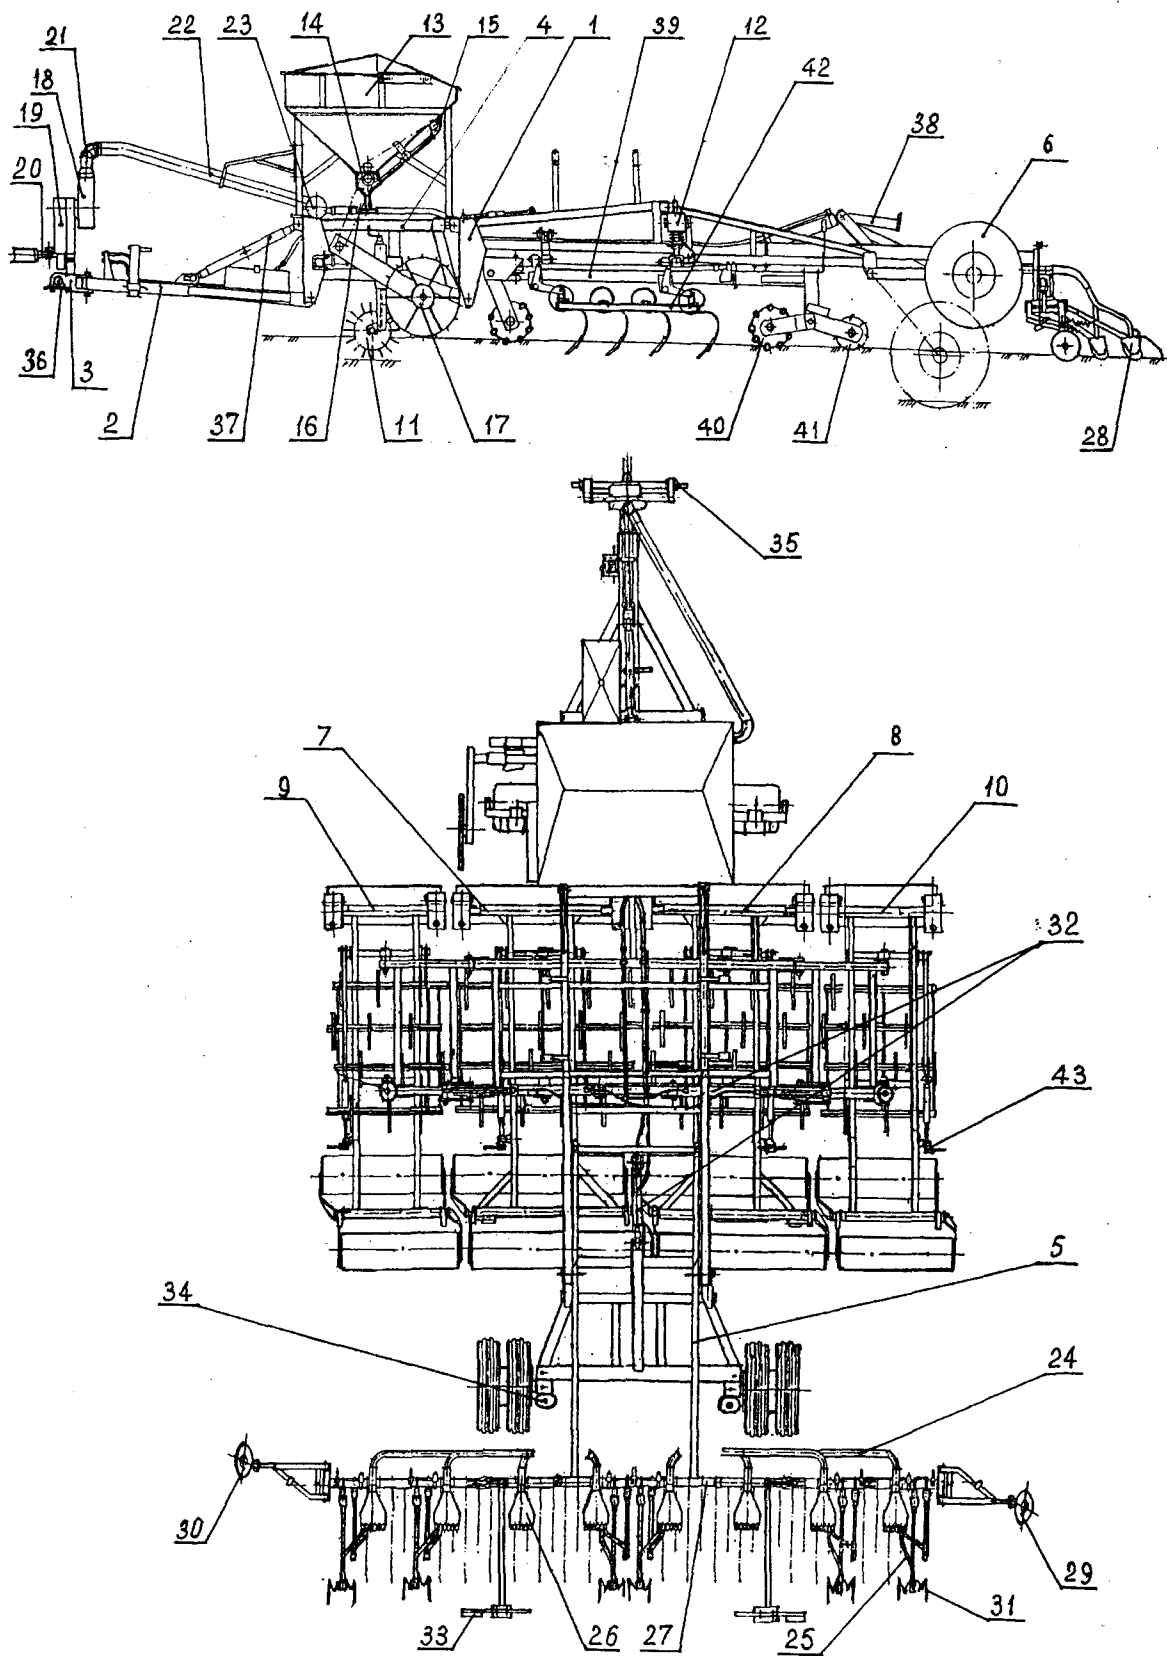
Комбинированный почвообрабатывающе-посевной агрегат АПП-6
